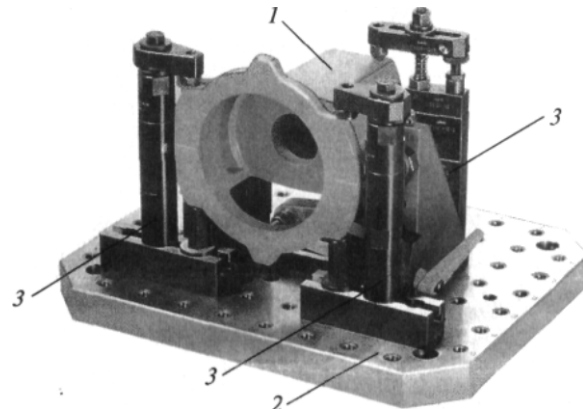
Затискна частина свердлильного пристосування багаторазового застосування: 1 – заготовка; 2 – основа; 3 – прихвати
